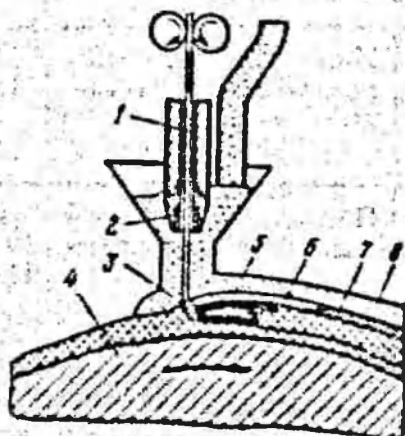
Схема процесса автоматической наплавки под флюсом
